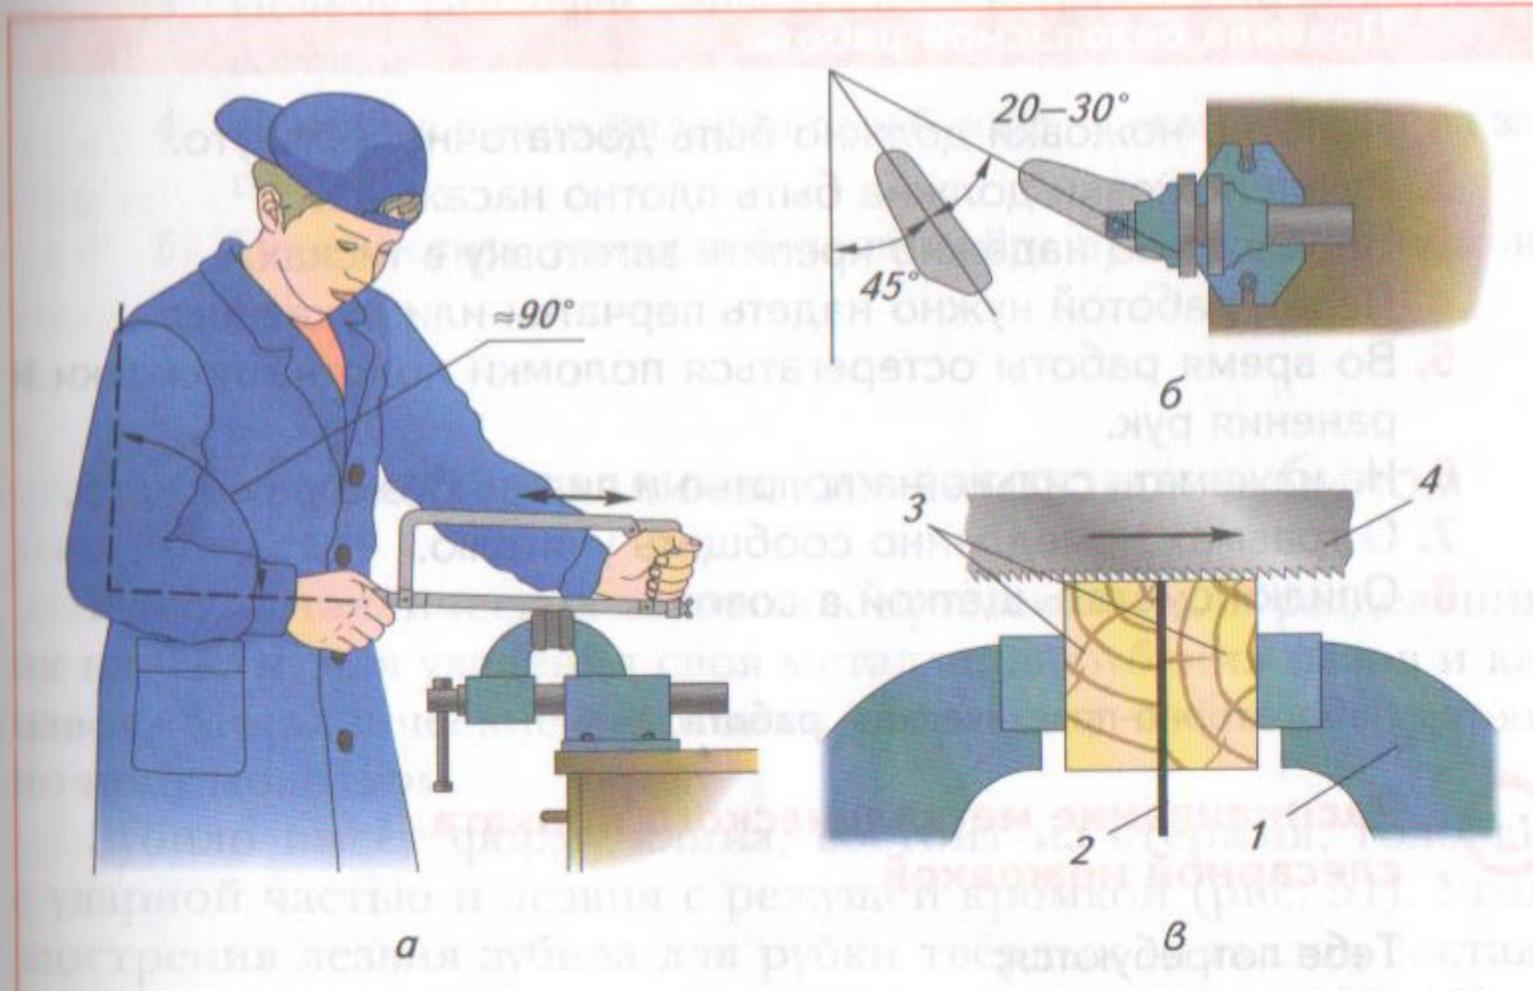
Приём пиления слесарной ножовкой: а — поза при пилении; б — положение ступней ног; в — распиливание тонкой металлической заготовки в тисках с её зажатием между деревянными брусками: 1 — тиски, 2 — распиливаемый лист, 3 — деревянные бруски, 4 — полотно пилы
